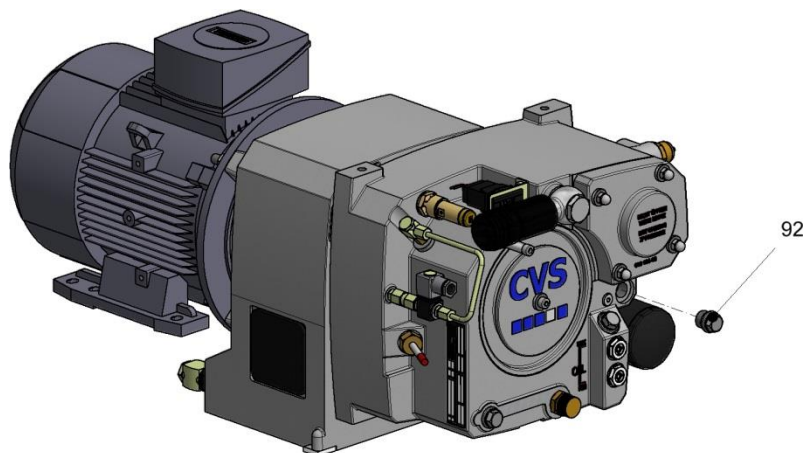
Verschlusschraube (Pos. 92) herausschrauben
